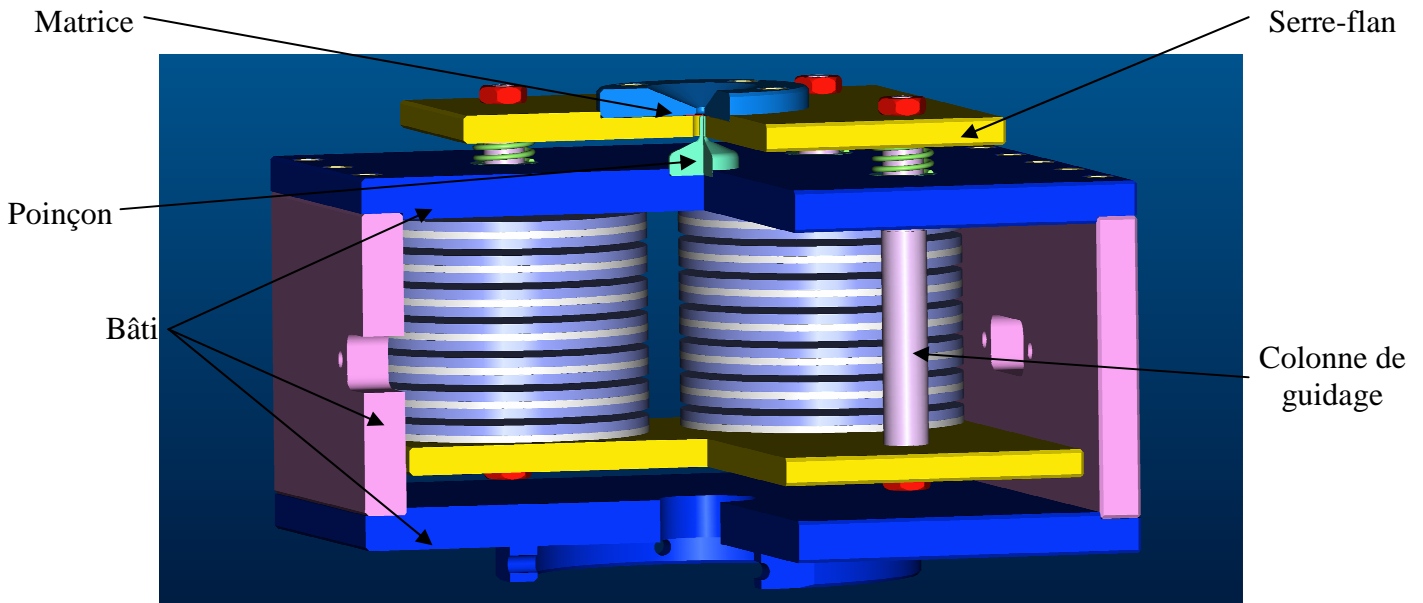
Vue en coupe du modèle 3D de la machine de test d'Erichsen modifié (dimensions enveloppes : $100 \times 100 \times 65 \text{ mm}^3$).
